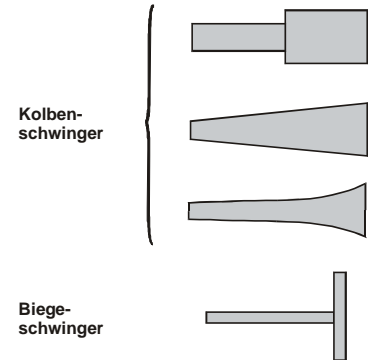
Formen mechanischer Ultraschallwandler.
